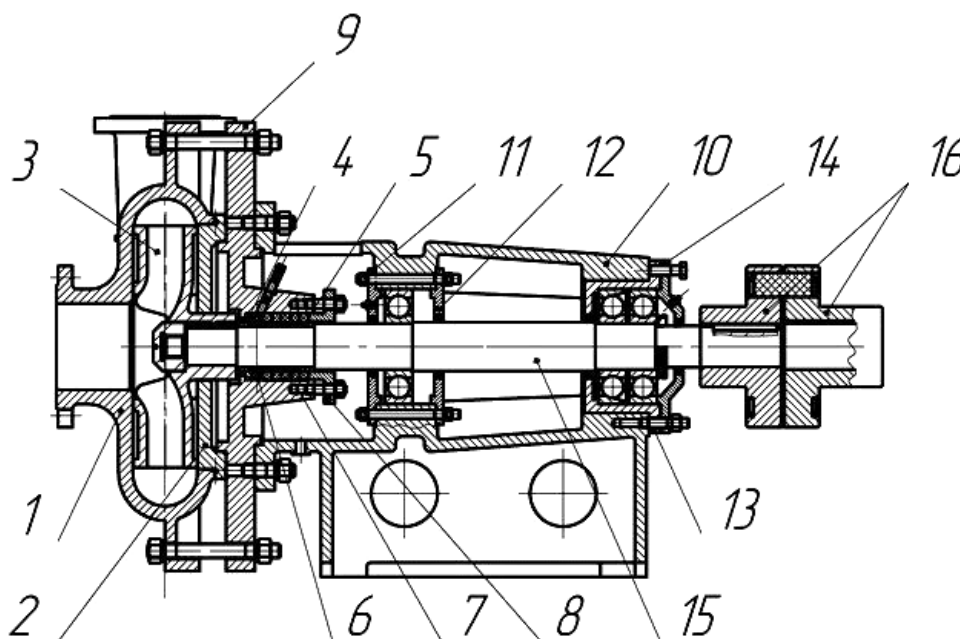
Общий вид насоса: 1 – корпус насоса; 2 – диск защитный; 3 – колесо рабочее; 4 – втулка сальника; 5 – втулка защитная; 6 – кольцо сальника; 7 – набивка; 8 – крышка сальника; 9 – крышка; 10 – картер; 11 – крышка прижимная; 12 – крышка прижимная; 13 – гильза; 14 – крышка прижимная; 15 – вал; 16 – муфта
